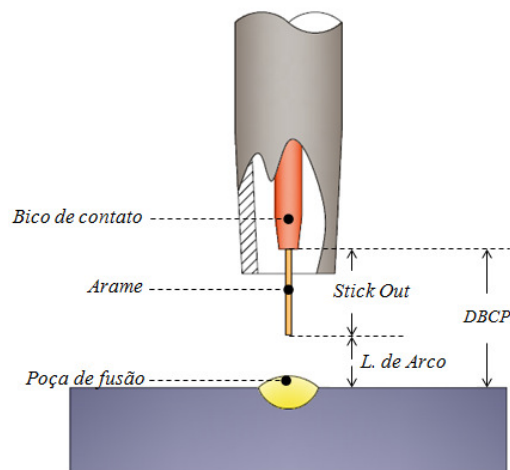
Desenho Esquemático de Processo de Soldagem
